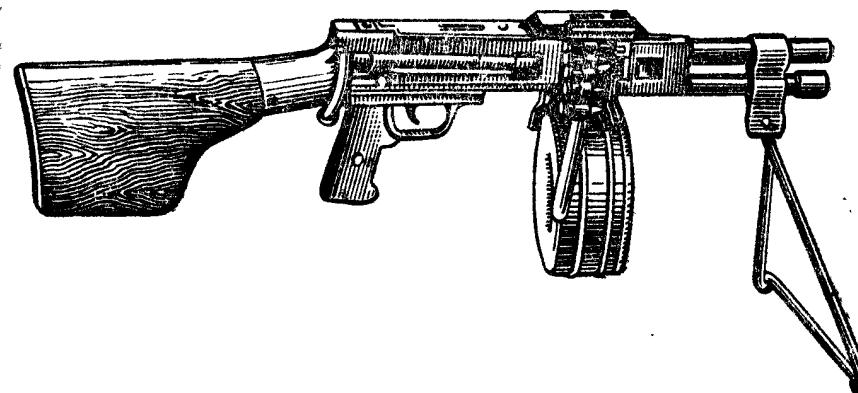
Станок с собранными частями и механизмами ручного пулемета Дегтярева (РПД)
